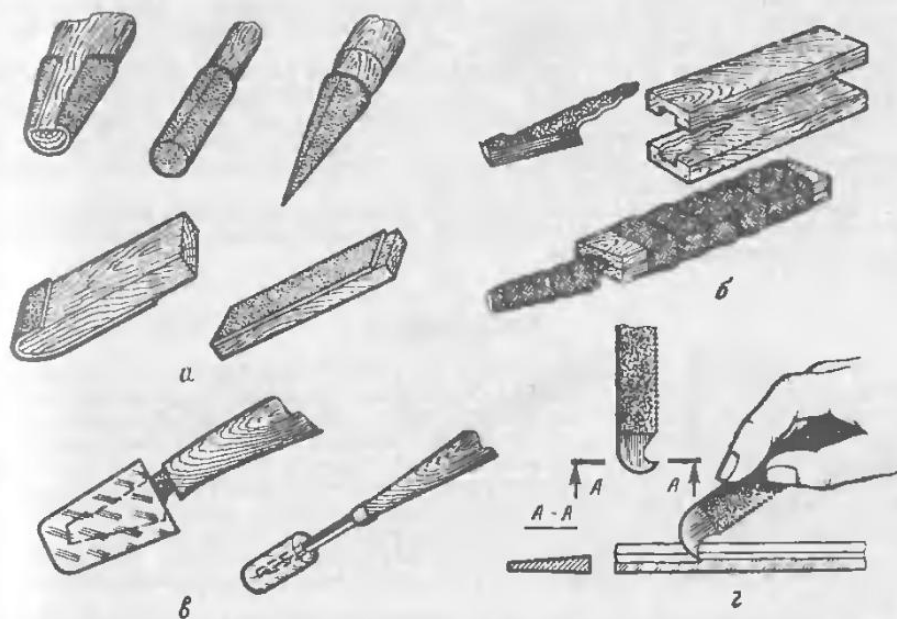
Шлифовальная шкурка, наклеенная на оправки различной формы: а - оправки с наклеенной шкуркой; б - заделка лезвия ножа в заготовку рукоятки; в - защитные чехлы для инструмента; г - резак для резки листового пластика
